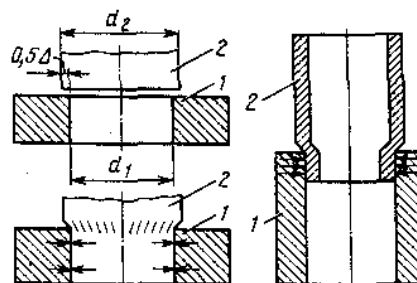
Последовательность схем соединений с нагревом охватывающей (1) или охлаждением охватываемой (2) детали
